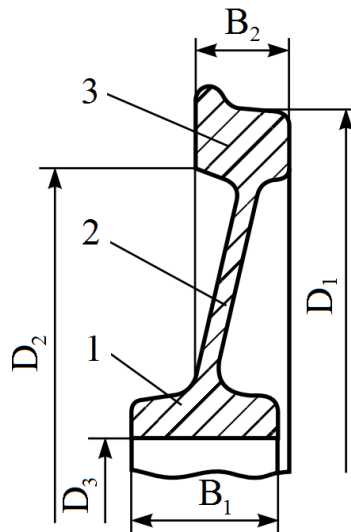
Колесо: 1 – маточина; 2 – диск; 3 – обід
